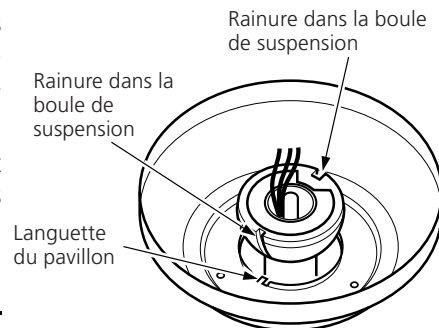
Languettes de pavillon et rainures dans la boule de suspension
